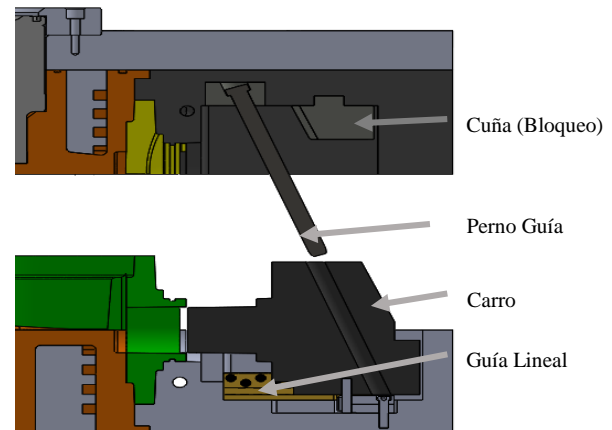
Diseño de molde con sistema mecánico de moldeo y liberación
